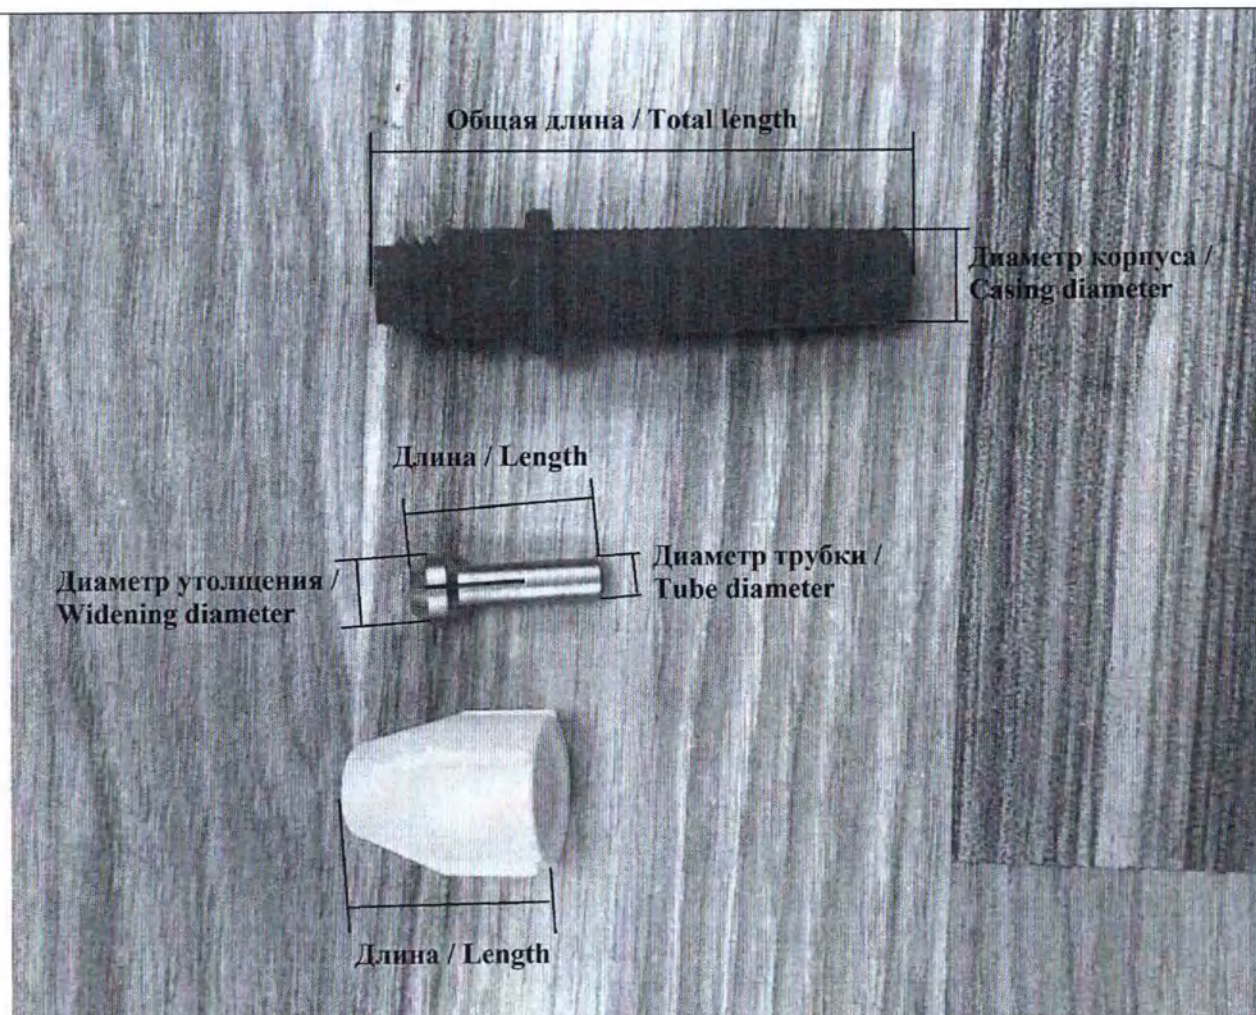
Поворотное устройство / Picture 5 Torque device
